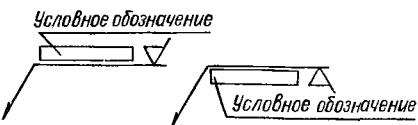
Обозначение контрольного комплекса шва сварного соединения
